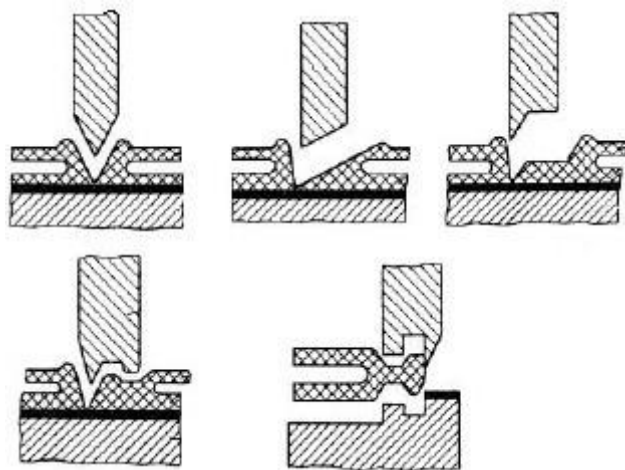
Формы рабочей части электродов для высокочастотной сварки с одновременным обрезанием изделия
